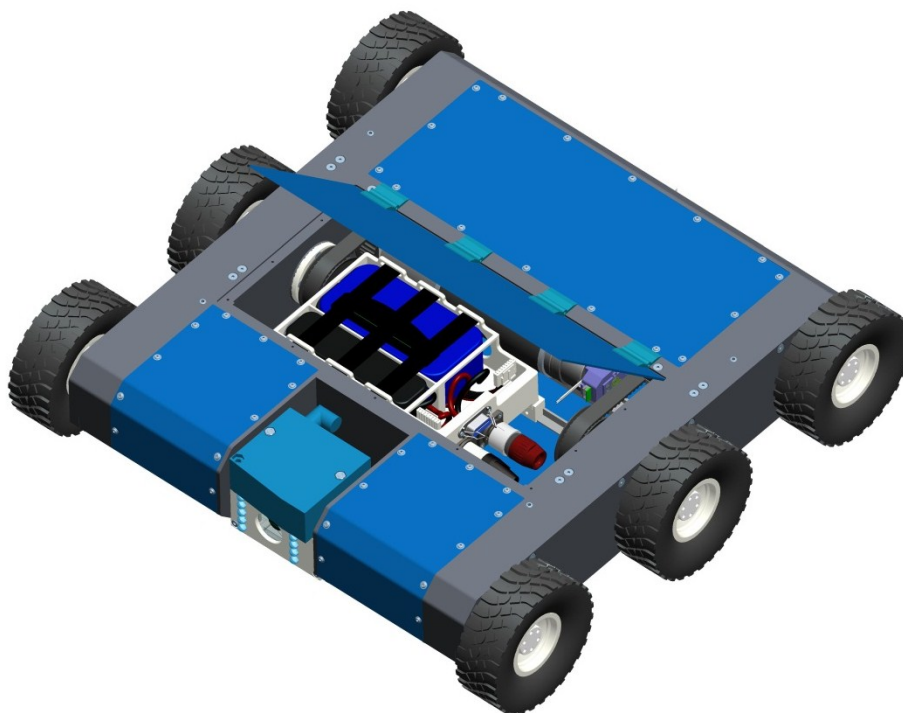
Kola vyplněné montážní pěnou - finální řešení
